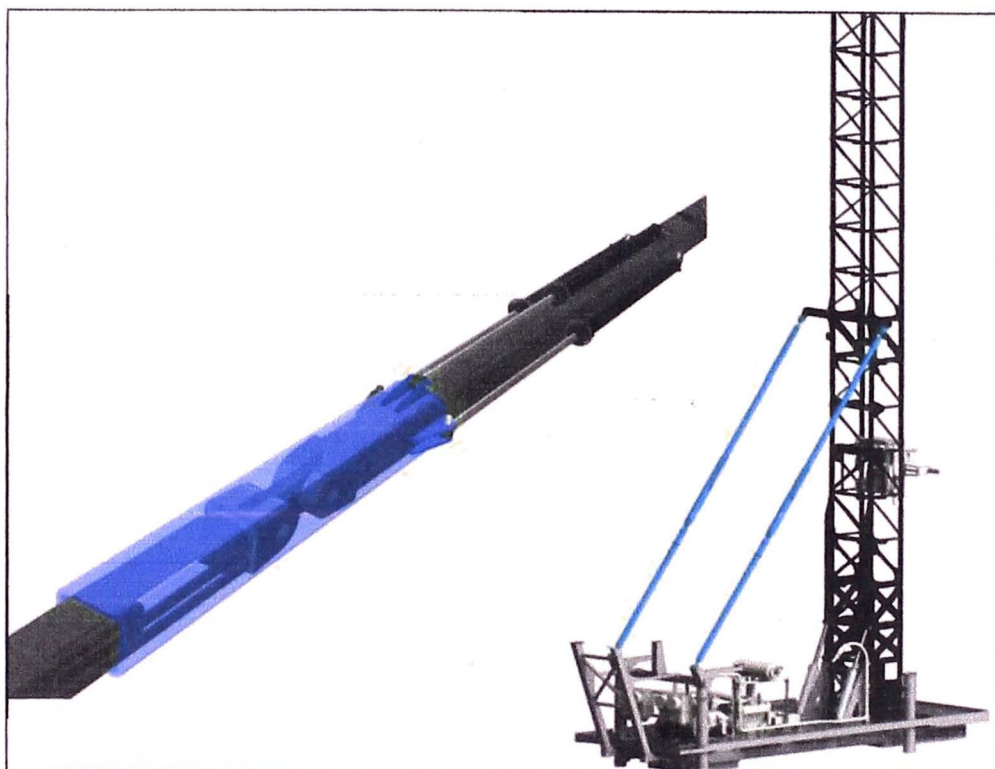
Apoyo articulado trasero & Collares de Bloqueo
